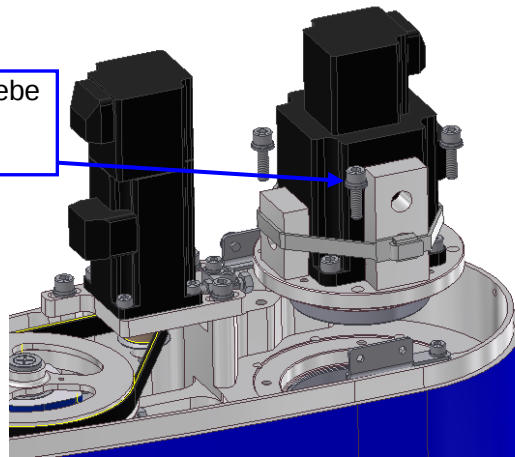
Entfernen des B-Achsenmotors und -getriebes
